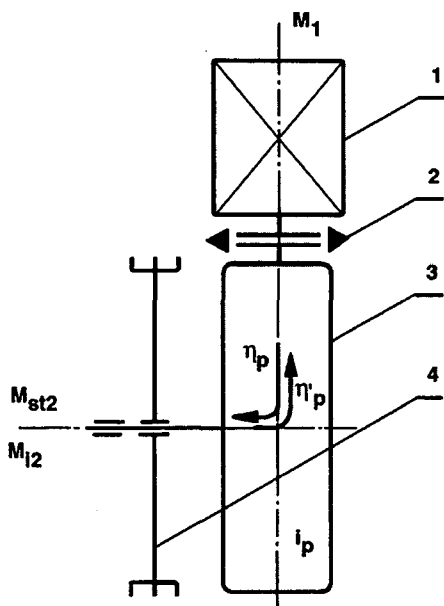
Схема для расчета M_1 : 1 – приводной мотор, 2 – тормоз, 3 – редуктор, 4 – тяговый шкив
